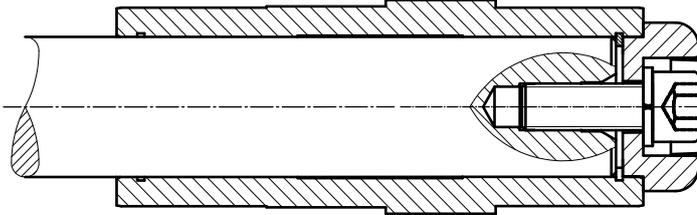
riduttore fissato ad un albero senza spallamento mediante elemento di fissaggio
